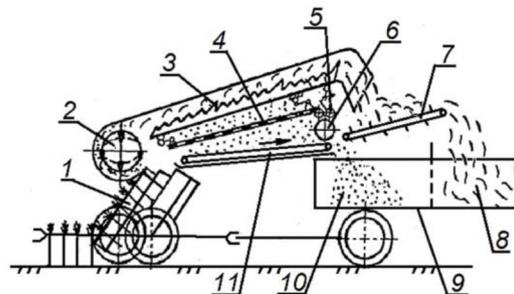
Льноуборочный комбайн с устройством отделения вороха от путанины: 1 – аппарат теробильный; 2 – аппарат очесывающий; 3 – сепаратор клавишный; 4 – решето плоское; 5 – терочный аппарат; 6 – сепаратор цилиндрический; 7 – транспортер путанины; 8 – путанина; 9 – транспортное средство; 10 – масса отсепарированная; 11 – транспортер отсепарированной массы
